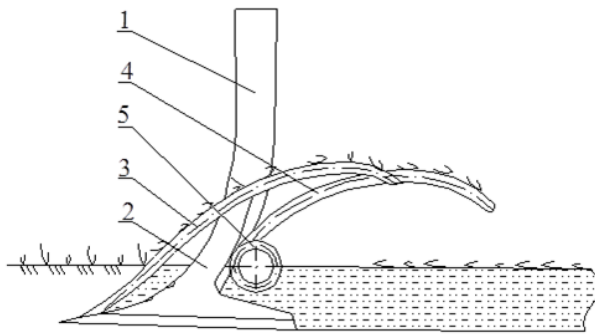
Схема робочого органа культиватора : 1 – стійка; 2 – плоскоріжуча лапа; 3 - роздвоєний стержень; 4 – підтримуючий стержень; 5 - кільцева пружина.
